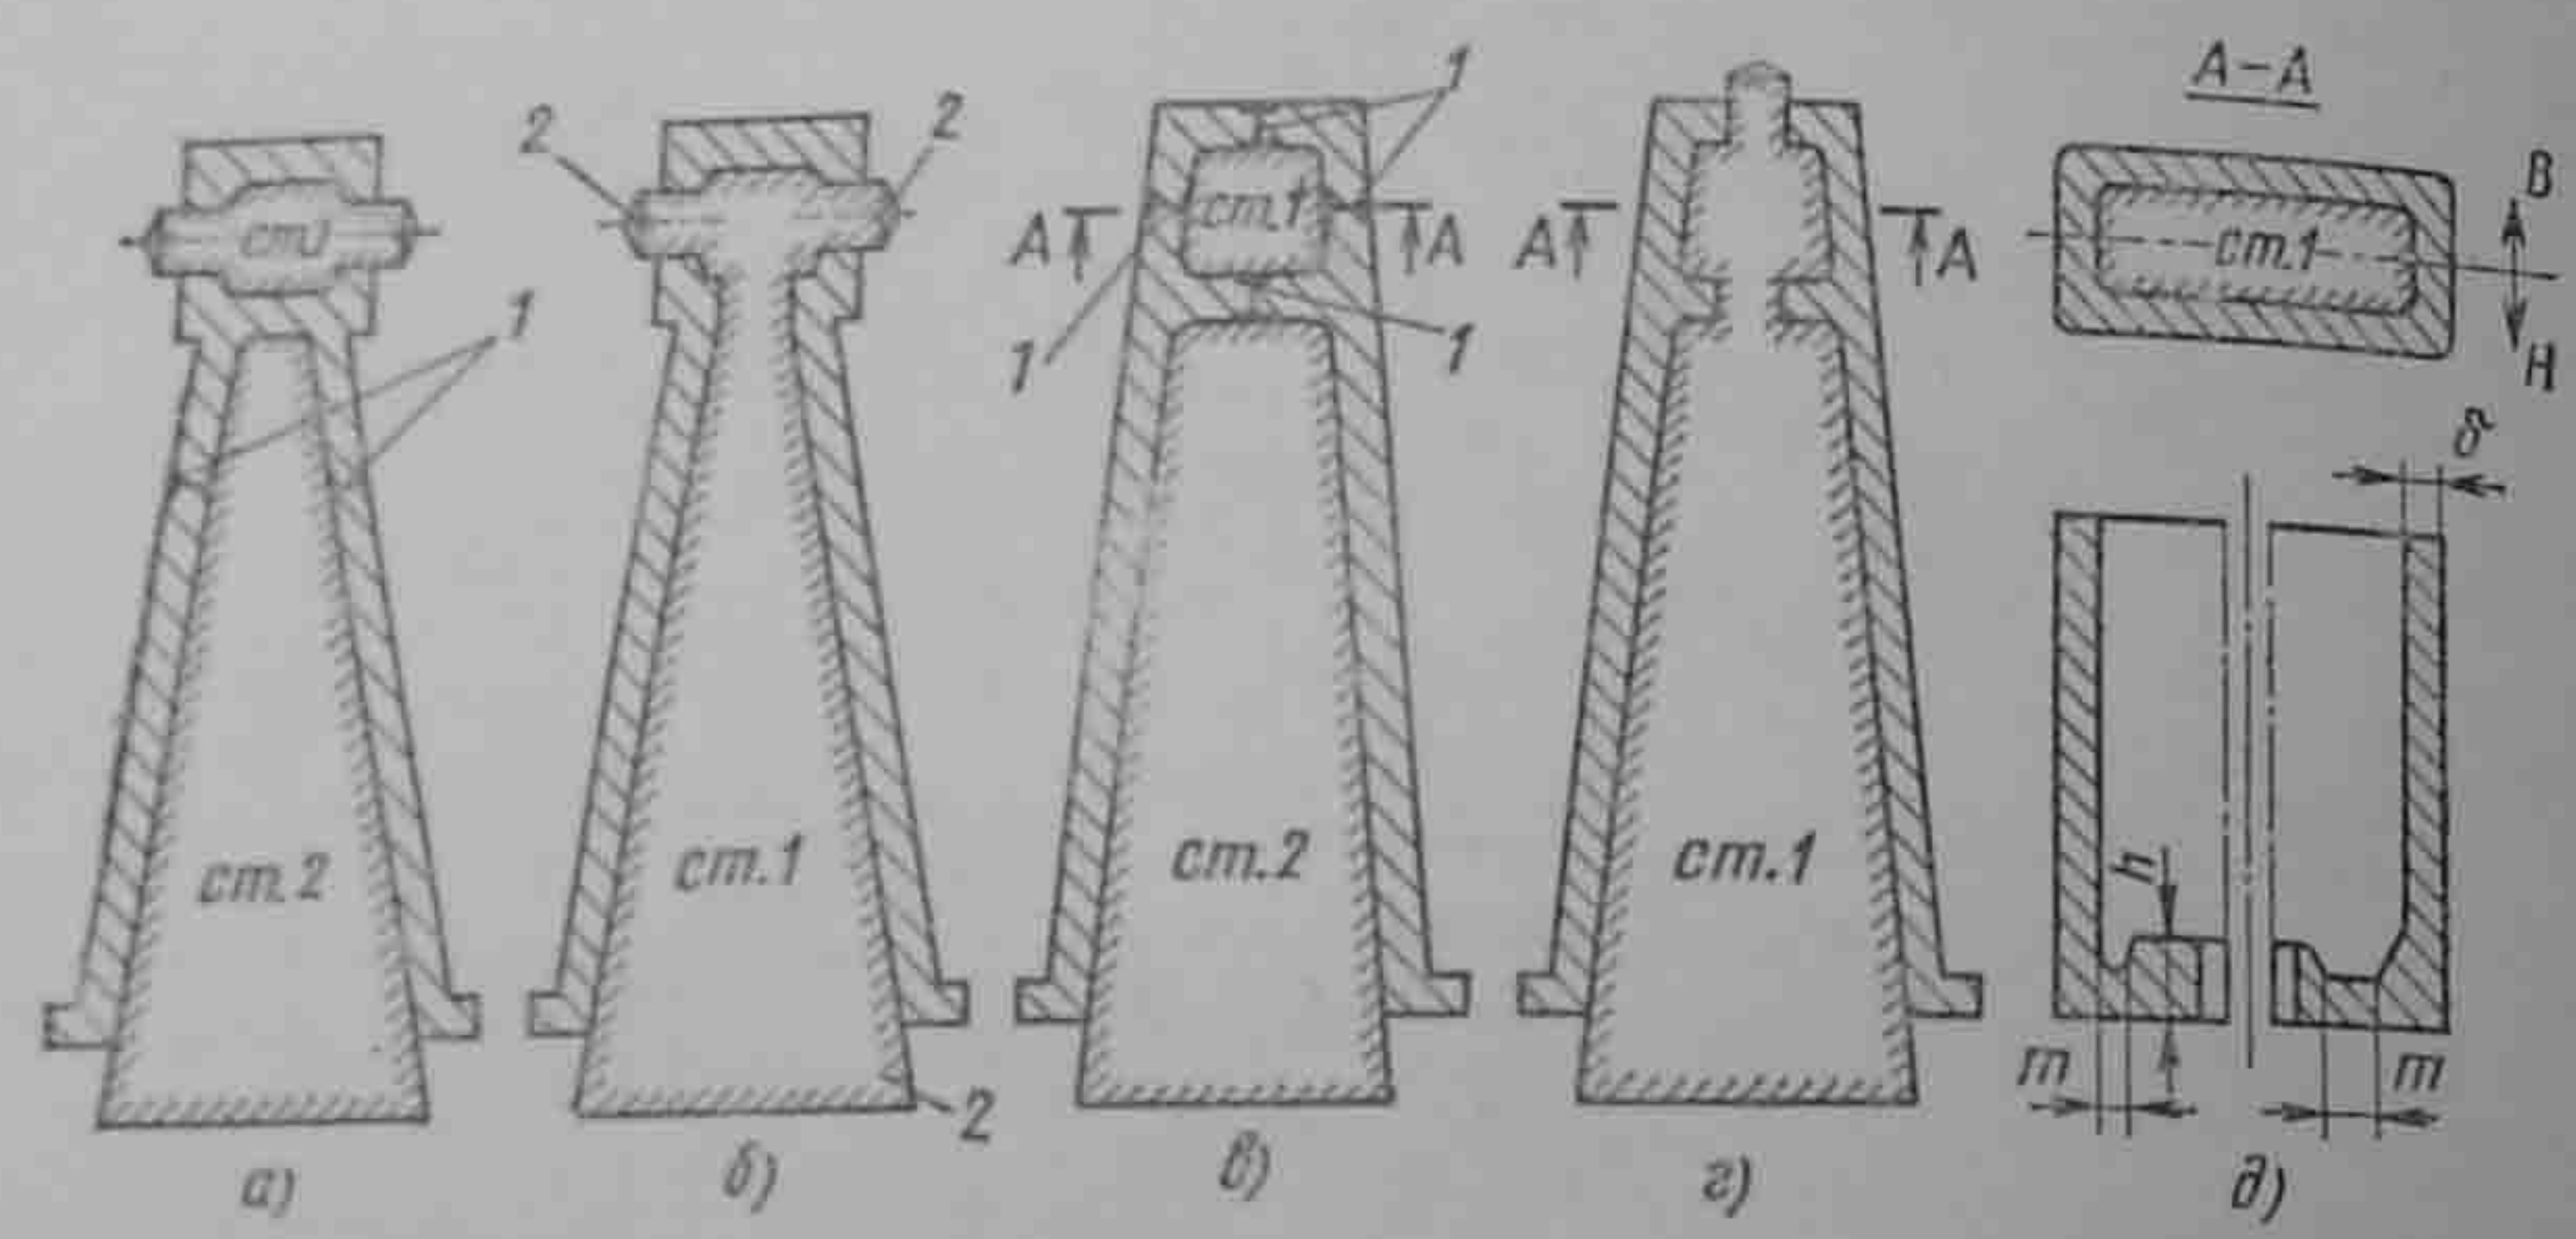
Изменение конструкции детали для облегчения крепления стержня в форме и предупреждения его разрушения в процессе заливки
